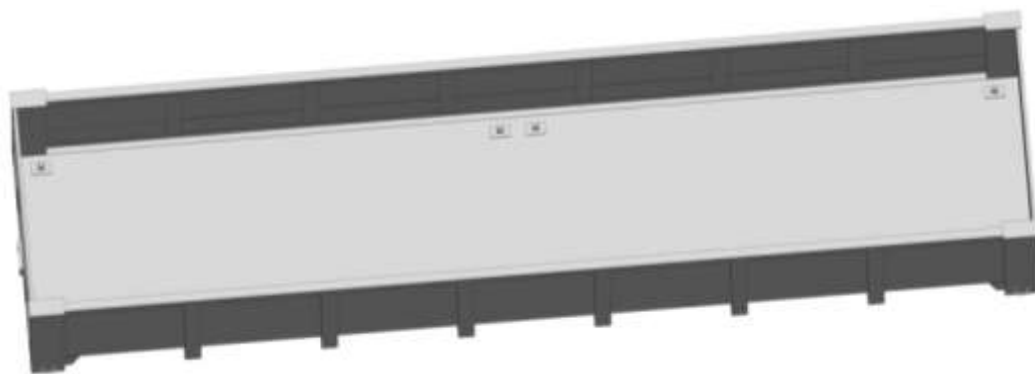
Просторова модель несучої конструкції напіввагона з фітинговими упорами
